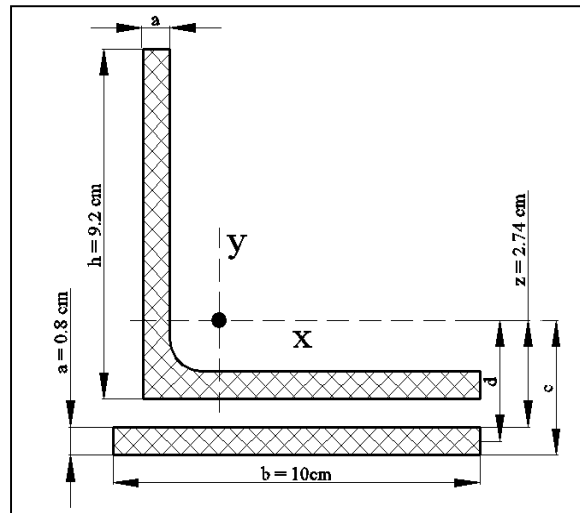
Dimensiones para el momento de inercia de la soldadura de la base
